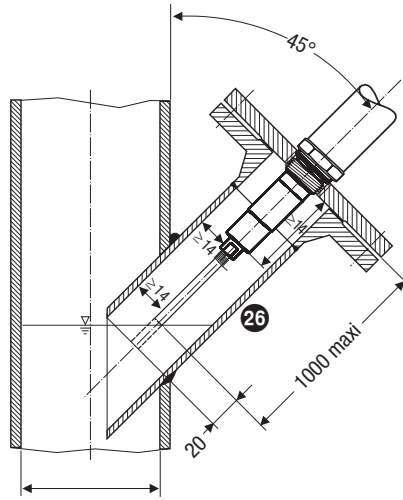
Montage en position inclinée, par ex. dans les conduites de départ montantes d'installations à eau surchauffée ou dans des réservoirs. Tubulure/ bride de raccordement DN 50
